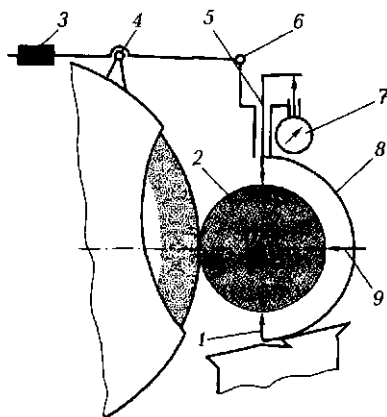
Схема устройства активного контроля для круглошлифовальных центровых станков:
